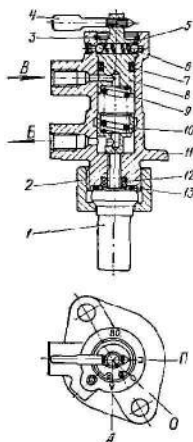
Включатель гидромуфты: 1 — термосиловой элемент; 2 — гайка; 3—упорное кольцо; 4—рычаг; 5 — пружина фиксатора; 6 — шарик; 7, 12 — уплотнительные кольца; 8 — пробка переключения режимов; 9 — возвратная пружина; 10 — золотник; 11—корпус; 13 — регулировочные прокладки; А — подвод масла, Б—отвод масла.
